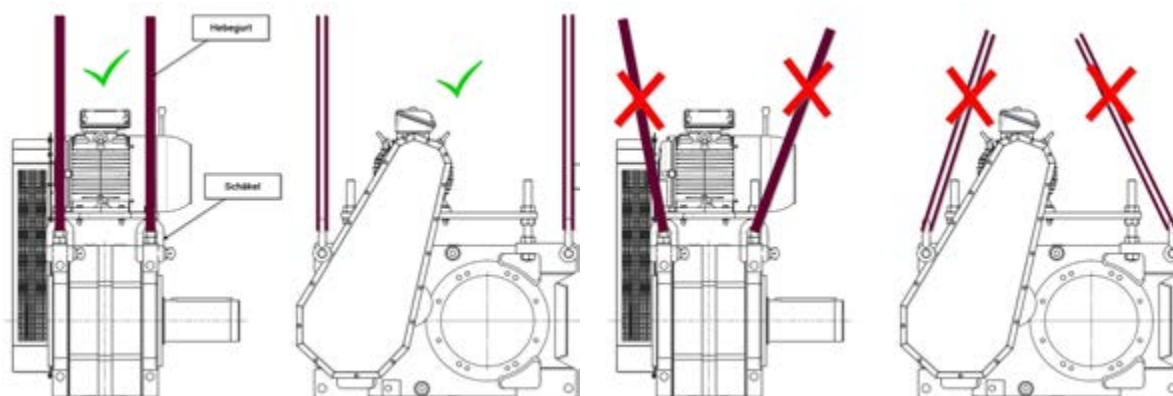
Транспортировка редуктора вместе с клиноременной передачей
